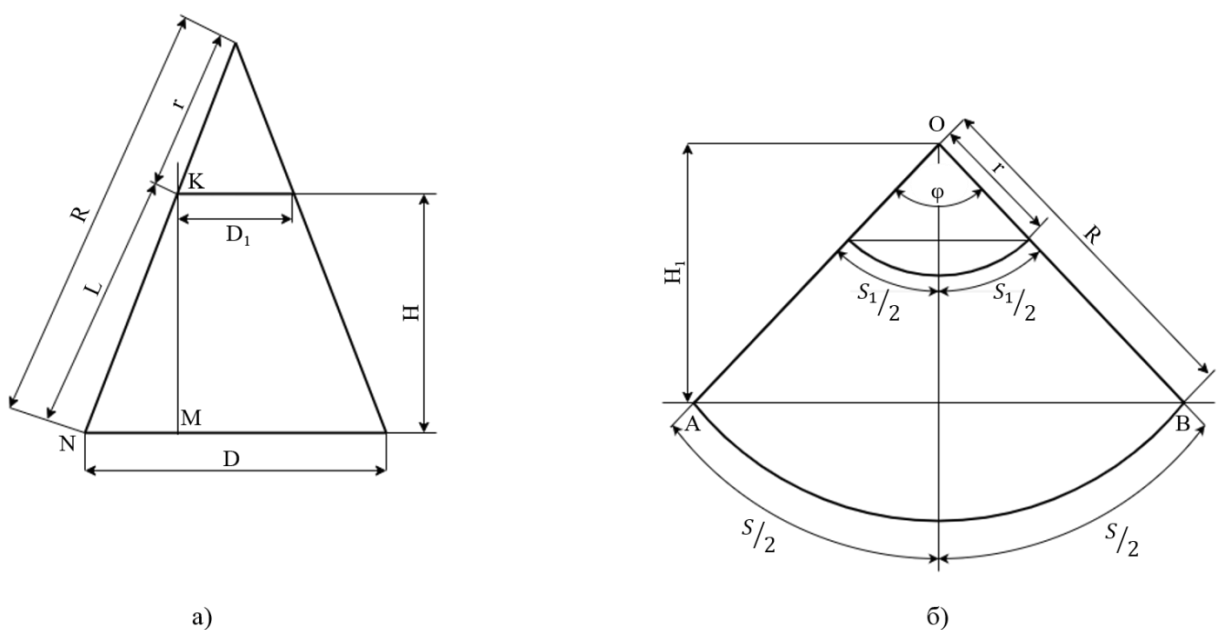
а) Усеченный конус; б) развертка усеченного конуса.
